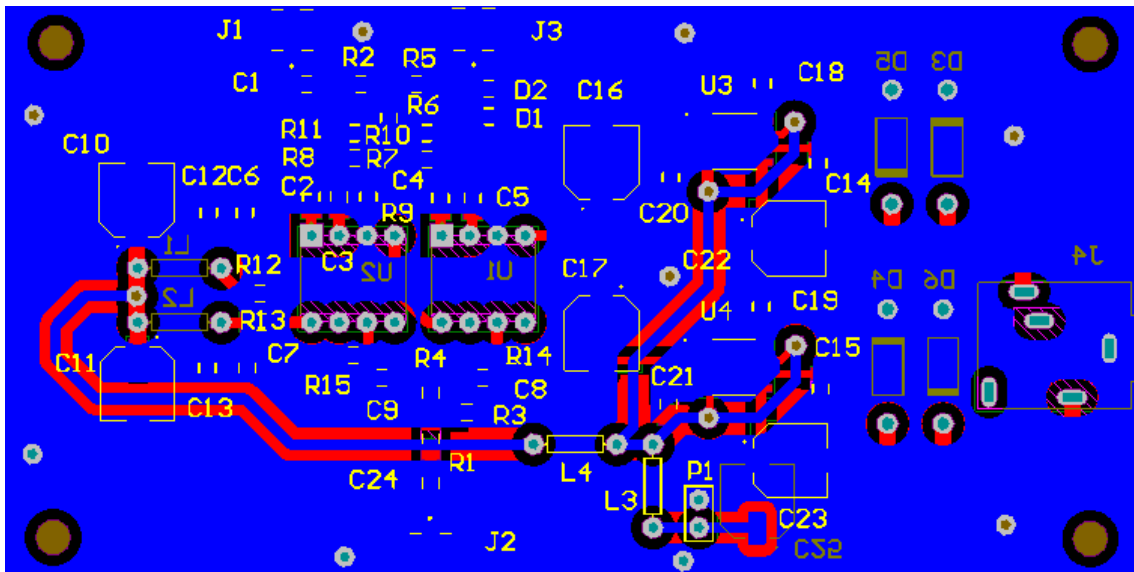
Diseño de pcb de la capa inferior del medidor de impedancias
